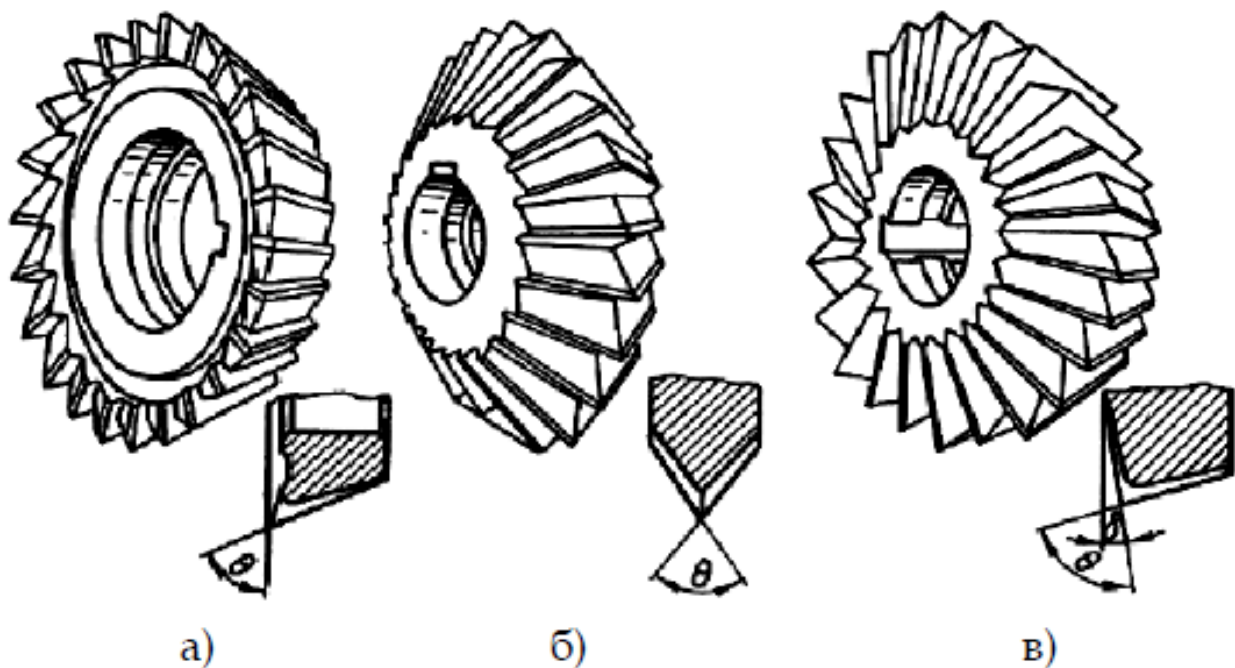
Фрезерування похилих площин кутовими фрезами
